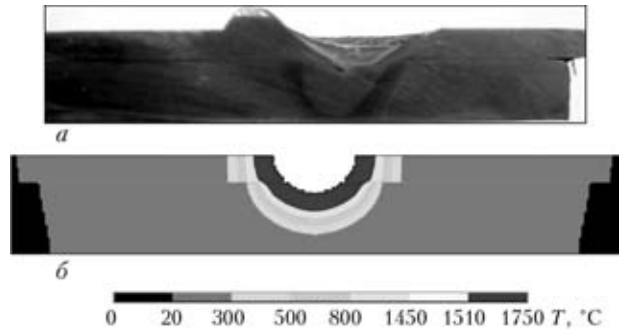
Макрошлиф точечного сварного соединения (а) и математическая модель, учитывающая выливание части расплавленного металла после прожигающего сварочного цикла (б)
